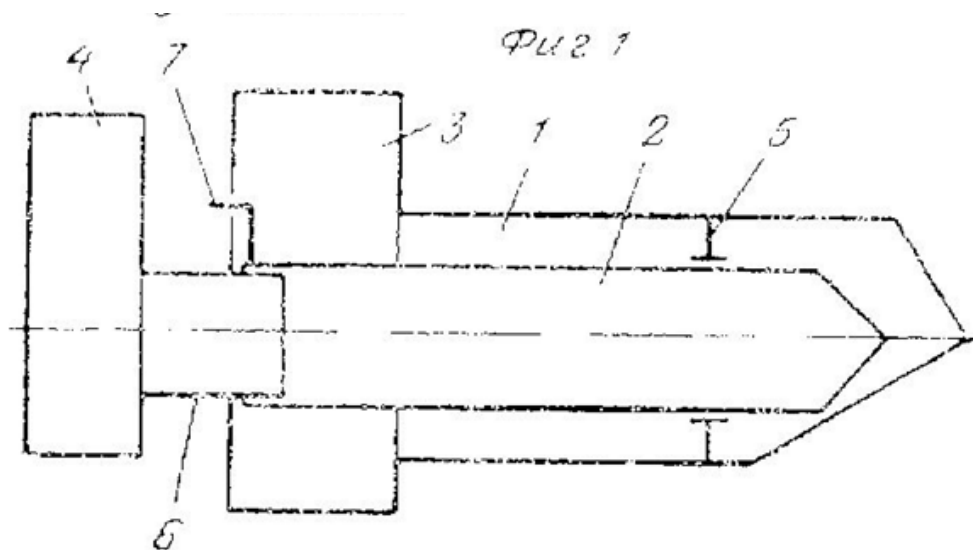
Горелка с двусторонними косыми срезами (1 – корпус; 2 – внутренняя труба; 3 – завихритель вторичного воздуха; 4 – завихритель первичного воздуха; 5 – направляющее кольцо; 6 – патрубок завихрителя; 7 – поворотное устройство)
